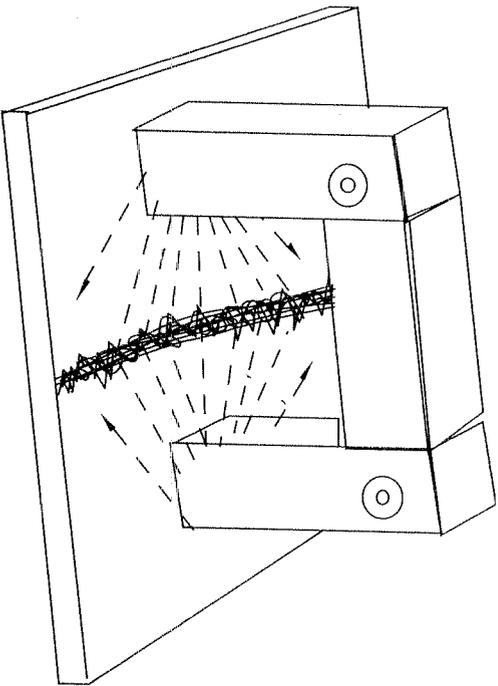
MAGNETIZACIÓN DE UNA SOLDADURA POR MEDIO DE UN YUGO DE ELECTROIMÁN
